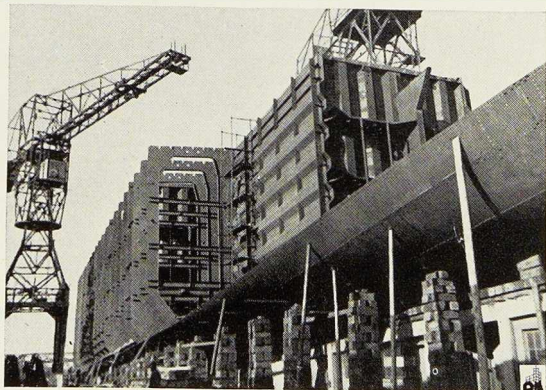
Vue d'ensemble de l'assemblage des éléments soudés et préfabriqués sur la coulisse de montage d'un pétrolier de 16.000 t (chantier John Cockerill).
